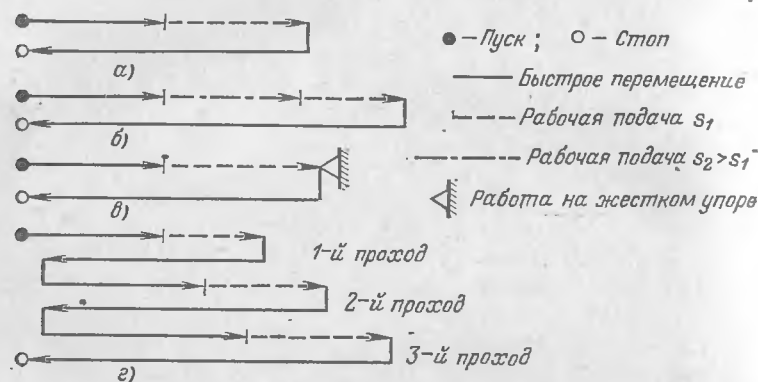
Схемы циклов движений силовых головок агрегатных станков.
